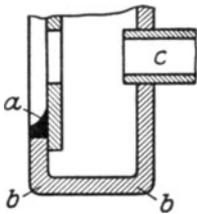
Unterer Teil einer neueren Ausführung der Wasserkammer. Die älteren Wasserkammern haben bei b Schweißstellen, die schwierig auszuführen waren und durch Aufreißen zu Kesselexplosionen Anlaß gaben. Die Schweißstelle a der neueren Wasserkammern ist sicherer herzustellen, c = die unterste Reihe der Siederohre.
